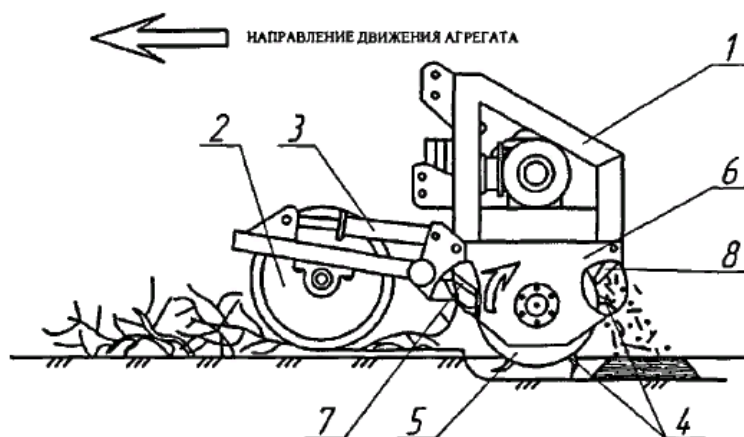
Схема машины для измельчения и заделки щепы в почву: 1 – рама; 2 – трамбовочный барабан; 3 – сервопривод; 4 – ножи; 5 – барабан; 6 – кожух; 7 и 8 – передние и задние контрножи
